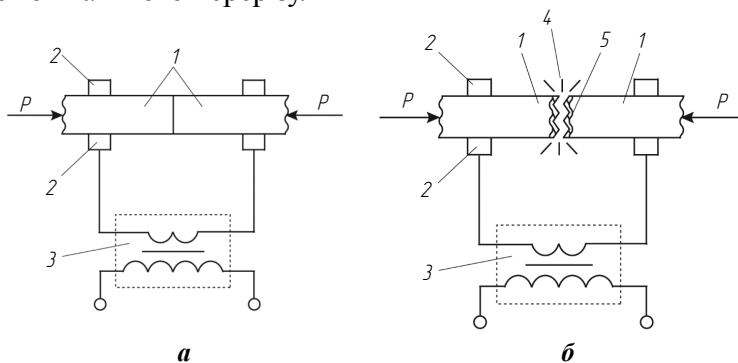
Схема стикового зварювання опором (*а*), стикового зварювання оплавленням (*б*)
